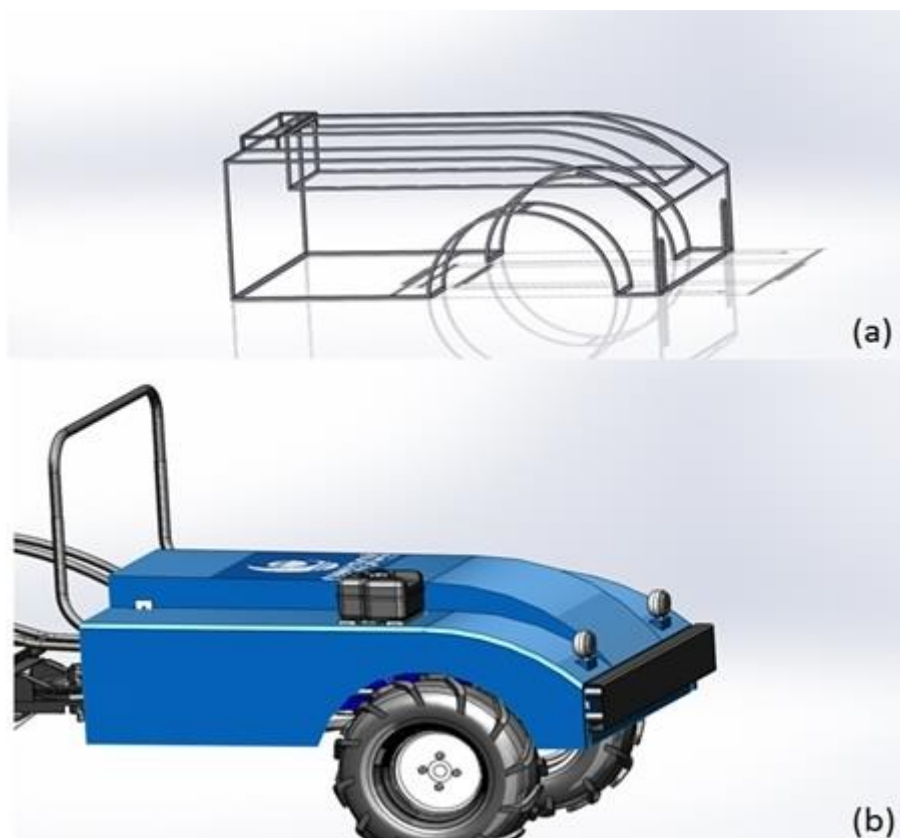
Desenhos do (a) vista tridimensional da estrutura para suporte da carenagem.; na figura (b) projeto do trator inteiro em CAD com a carenagem .
